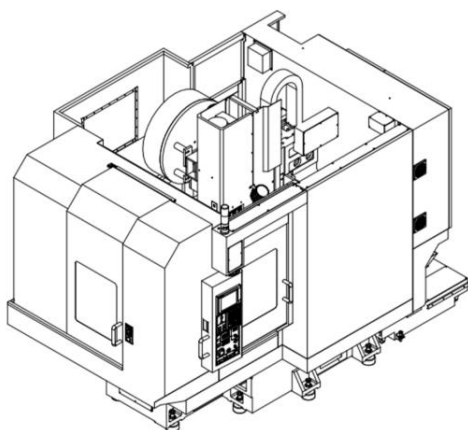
CNC OC MÜGA S 500 – pohled zleva [53]
